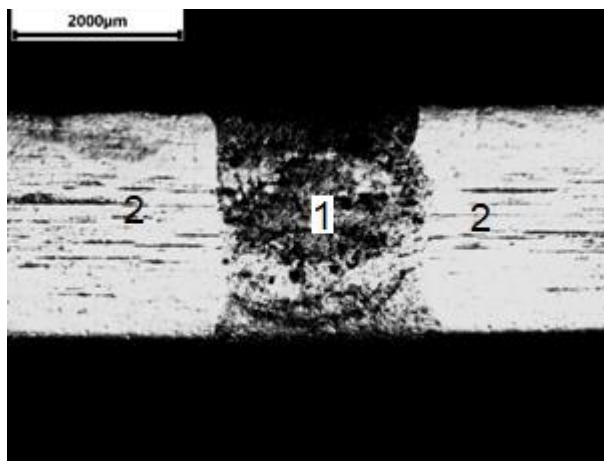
Макроструктура сварного соединения, выполненного способом лазерной сварки; мощность излучения 700 Вт: 1 – шов, 2 – основной металл
